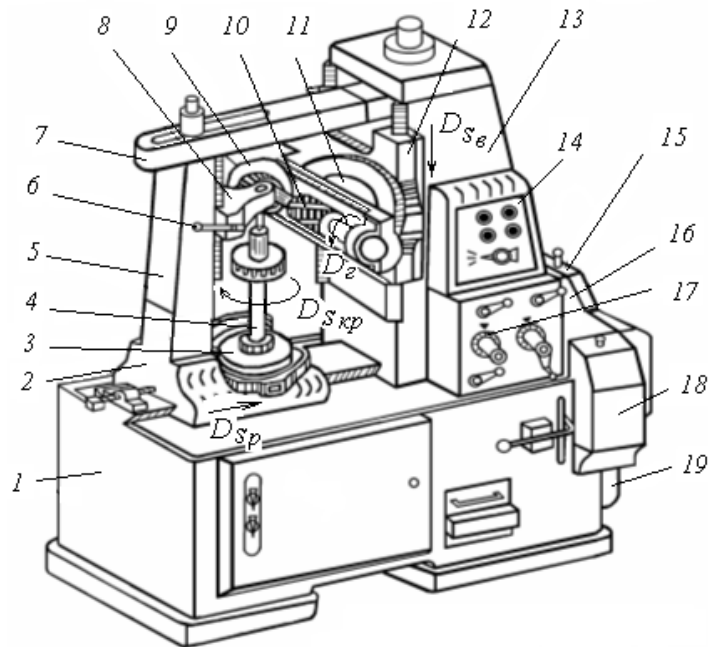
Внешний вид зубофрезерного станка модели 5310
